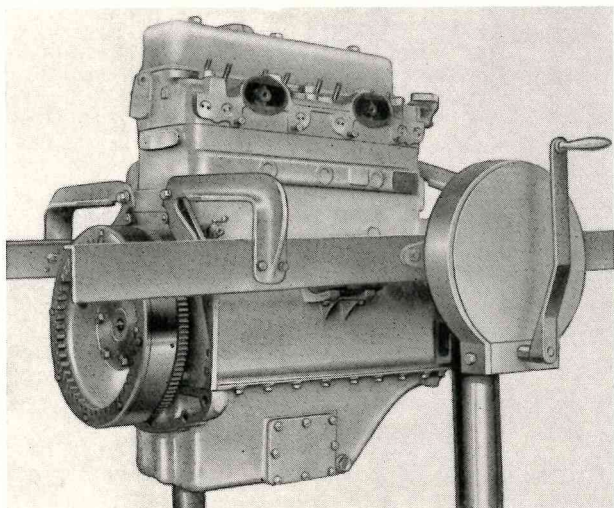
Vista lato destro del motore montato su cavalletto rotativo. (Notare il fissaggio delle staffe posteriori al cavalletto e al motore).
